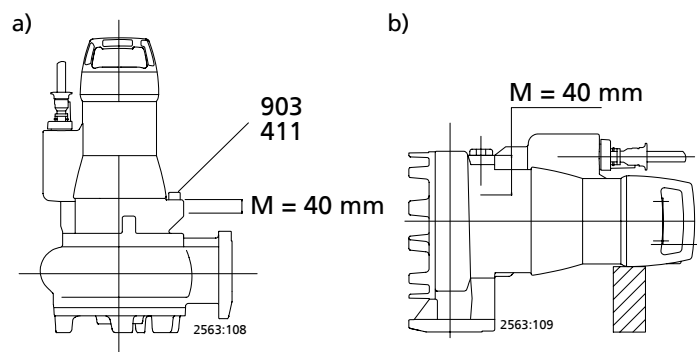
Llenado del líquido lubricante a) Modelos YL & WL; b) Modelo YL & WL para tamaños 50-170, 50-172 y 65-220
